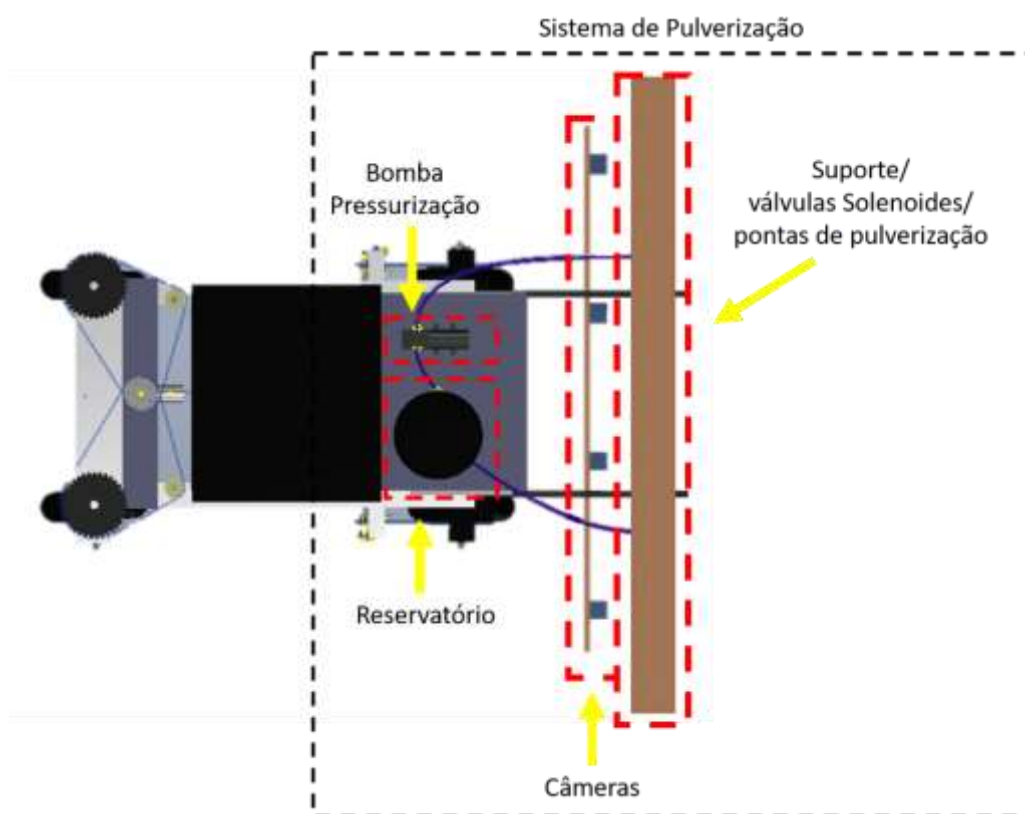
Sistema de pulverização seletiva construído no protótipo de pulverizador seletivo.
